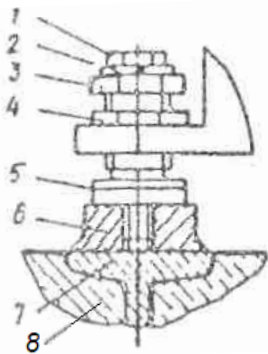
Винтовая опора крепления оборудования к балке фундамента:
